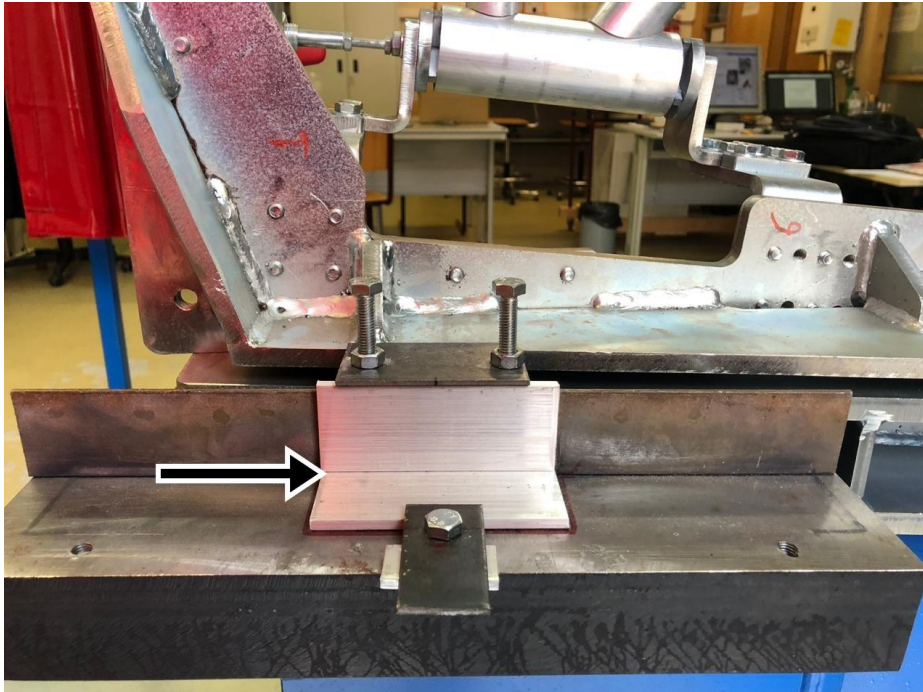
Fixação das chapas na mesa de soldadura. As chapas a soldar estão indicadas pela flecha
